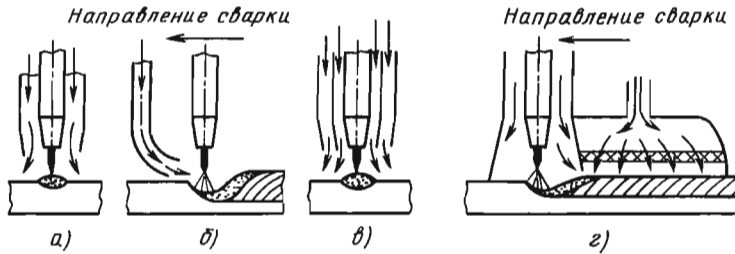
Схемы подачи защитного газа в зону плавления:
